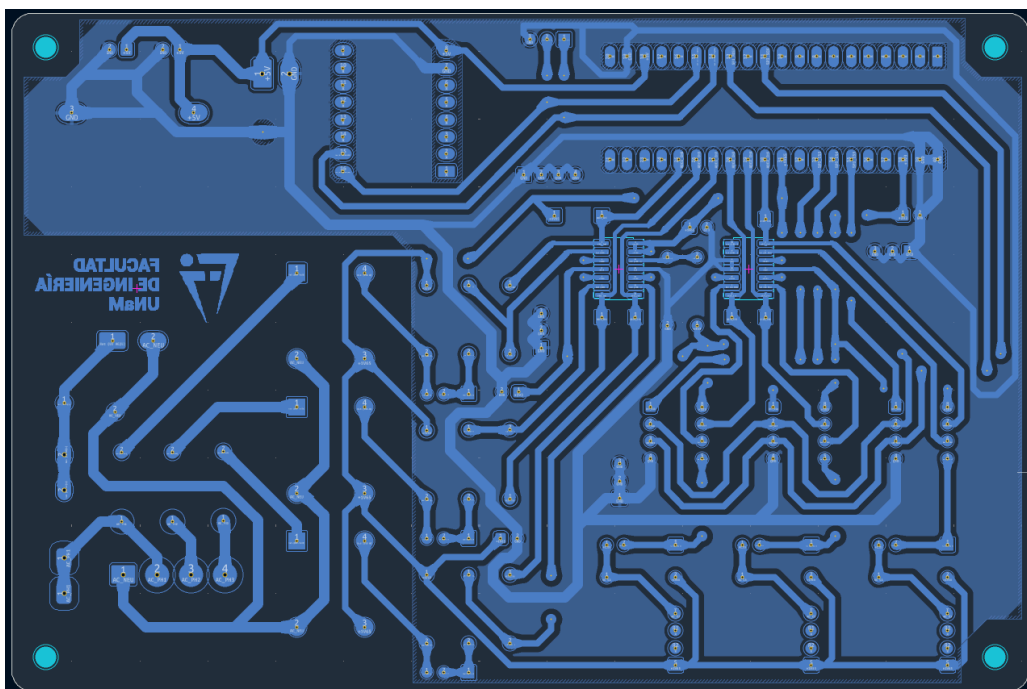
Ruteado de la capa inferior (Bottom Layer) de la PCB.
